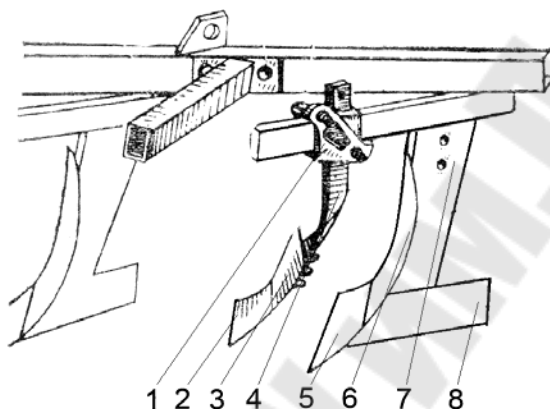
Рабочие органы плуга: 1 – детали крепления; 2 – лемех предплужника; 3 – отвал предплужника; 4 – стойка предплужника; 5 – лемех корпуса; 6 – отвал корпуса; 7 – стойка корпуса; 8 – доска полевая
